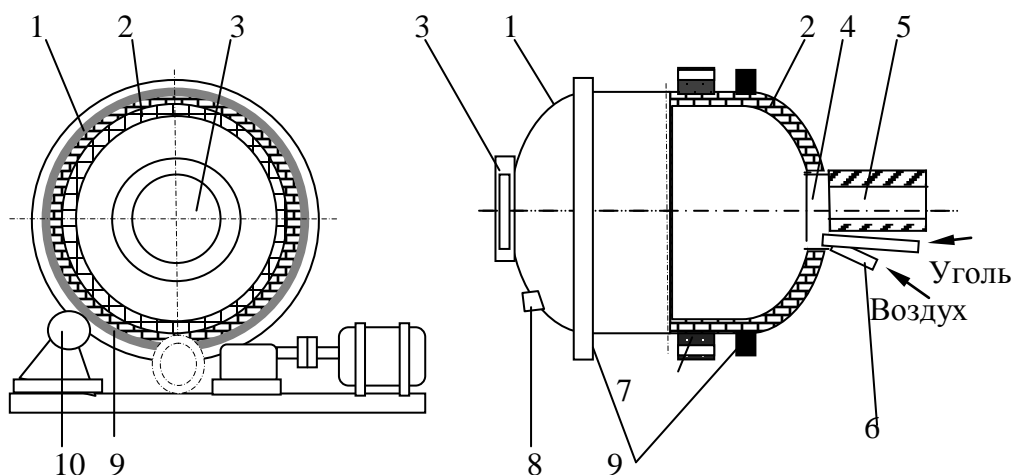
Схема короткобарабанной печи: 1 – стальной корпус; 2 – высокоглиноземистый кирпич; 3 – крышка загрузочного окна; 4 – топочное окно; 5 – боров для отвода печных газов; 6 – форсунка для подачи пылеугольного топлива и воздуха; 7 – венцовая шестерня; 8 – отверстие для выпуска продуктов плавки; 9 – бандаж; 10 – опорный ролик
